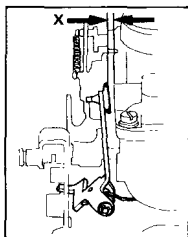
Регулировка клапана разбалансировки поплавковой камеры на карбюраторе Solex
